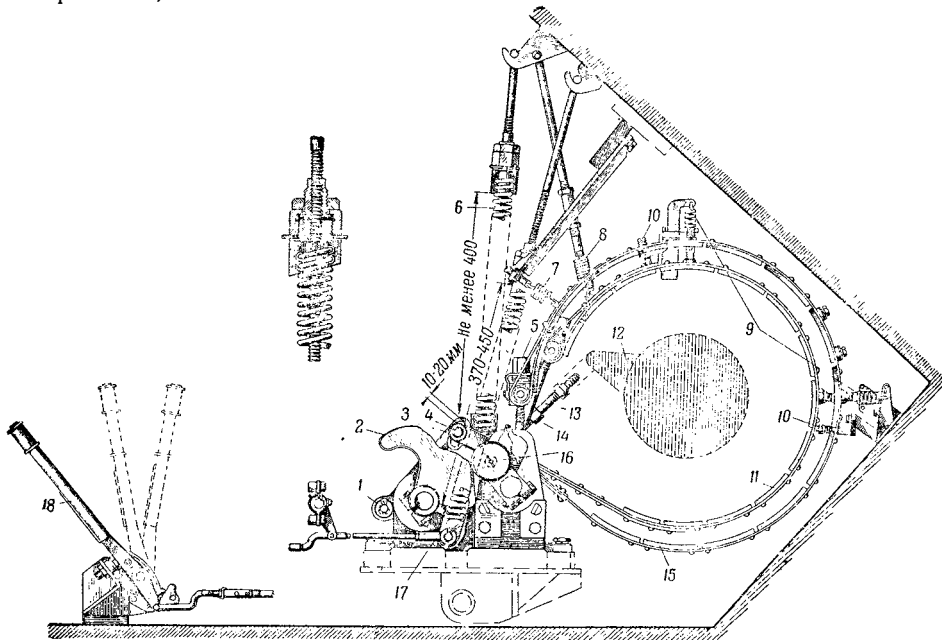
Привод управления планетарными механизмами и остановочными тормозами:
